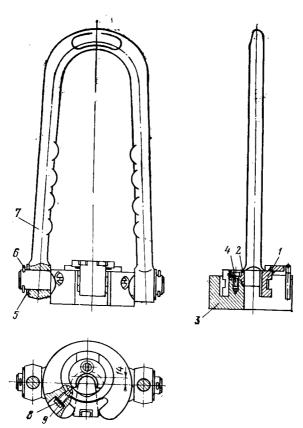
Элеватор штанговый ЭШН: 1- втулка; 2- корпус; 3- вкладыш; 4, 8- винты; 5- шайба; 6- шилинт; 7- серьга; 9 — шайба пружинная
